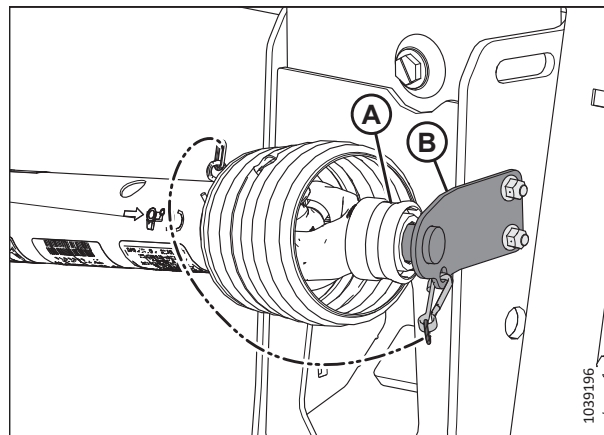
Prise de force en position de rangement – Prise de force B7038 ou B7039
